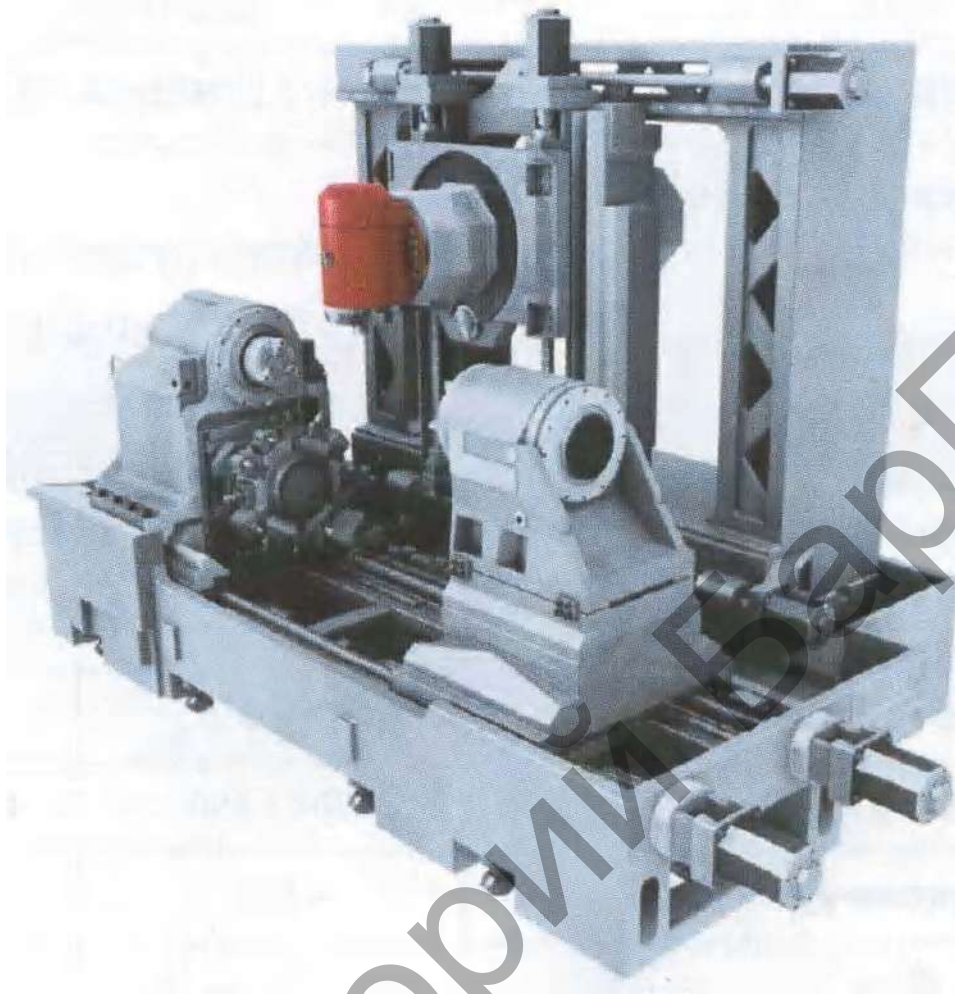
Токарно-фрезерный обрабатывающий центр модели NT4200DCG компании MORI SEIKI (Япония)
